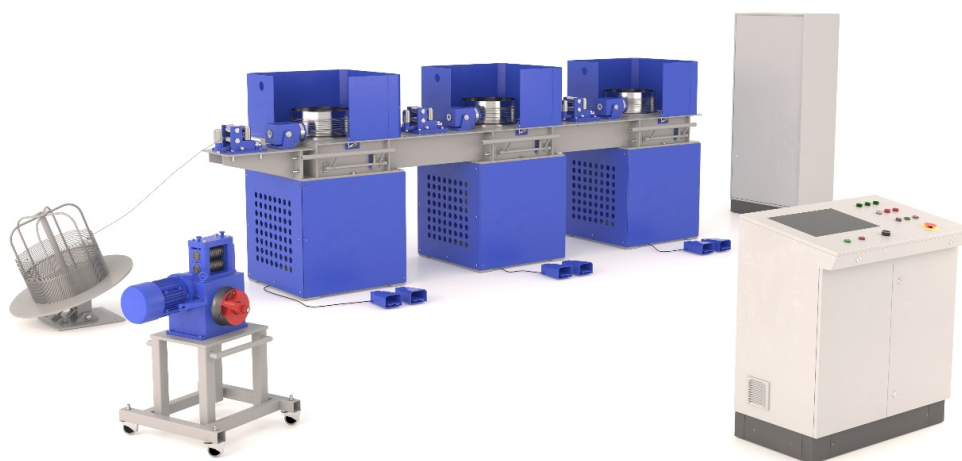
Общий вид прямомоточного стана ЮУрГУ
